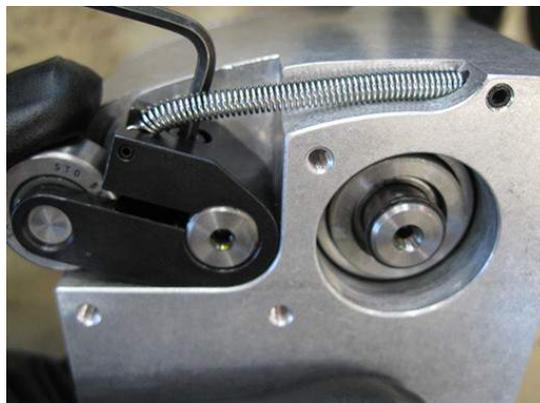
VIS DE SERRAGE DU BRAS À CAME
